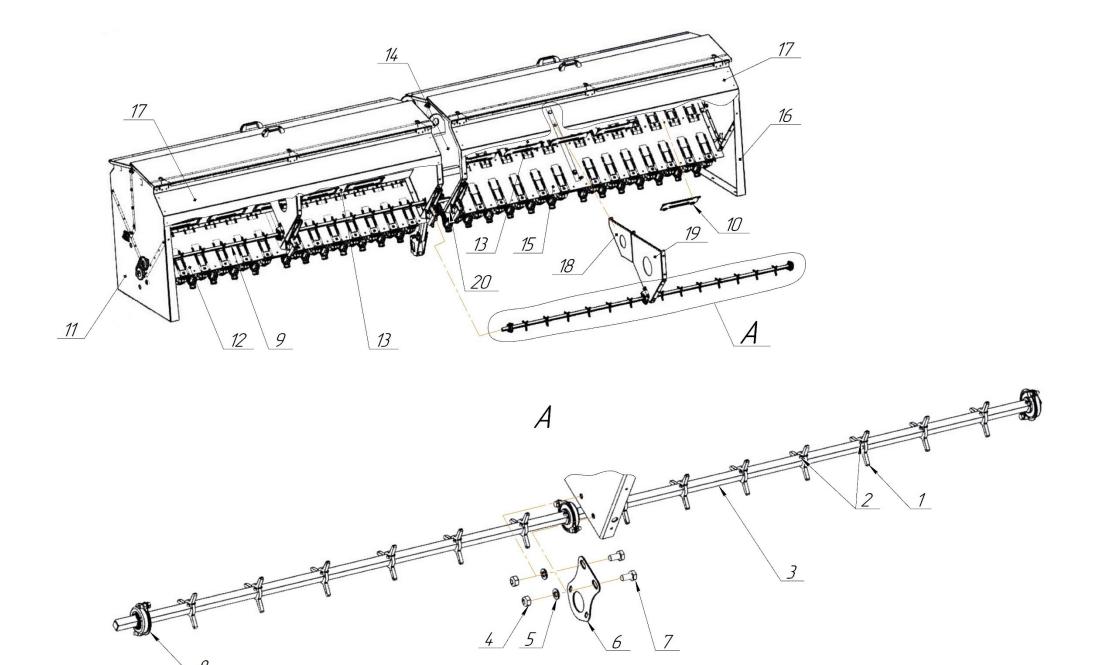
Валы ворошилок и стенки ящика 29
